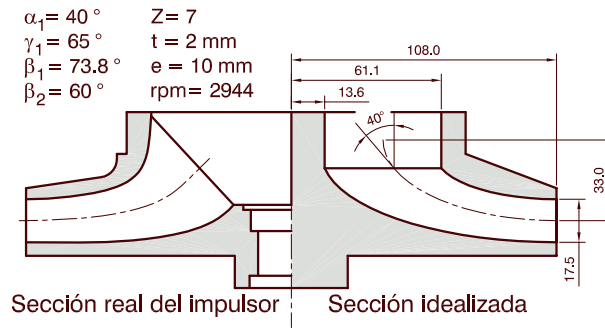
Dimensiones del impulsor de una bomba medida. Las dimensiones están en mm.
